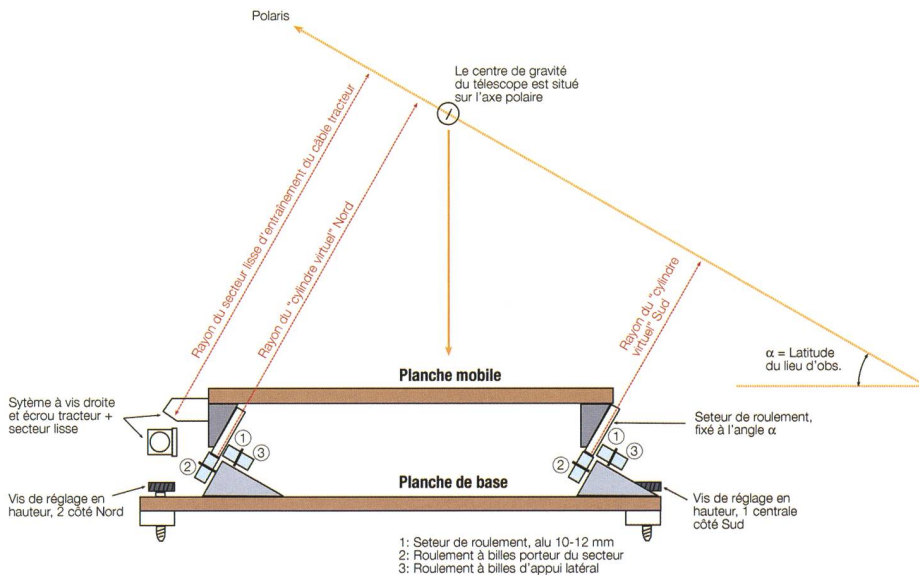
Vue latérale de la table équatoriale. (Dessin de Chuck Shaw, adapté par RD, redessiné par Thomas Baer)
